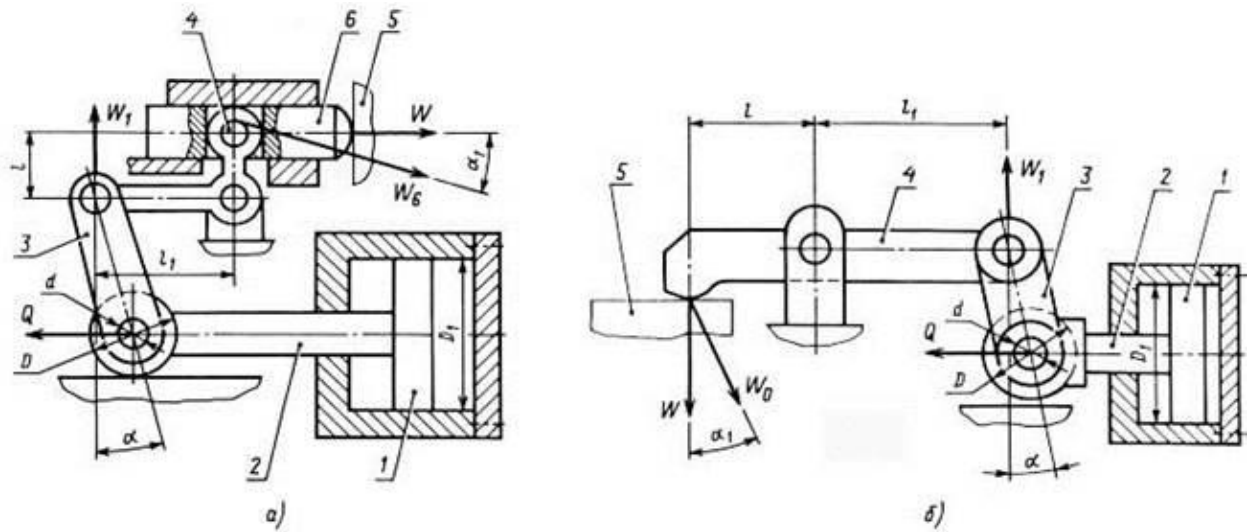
Конструктивні схеми важільних шарнірних механізмів-підсилювачів з пневмоприводом
